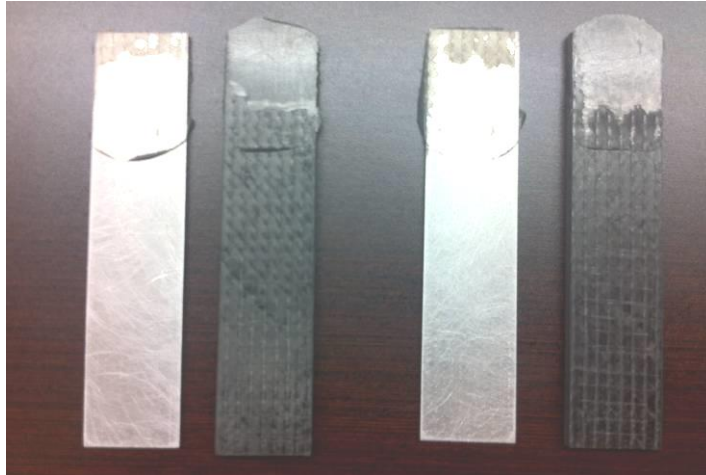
Imagen de probetas de aluminio 6061 T6 y CF-GF (izq.) y de aluminio 6061 T6 y CF-CF (der.) después del ensayo de adhesión.
